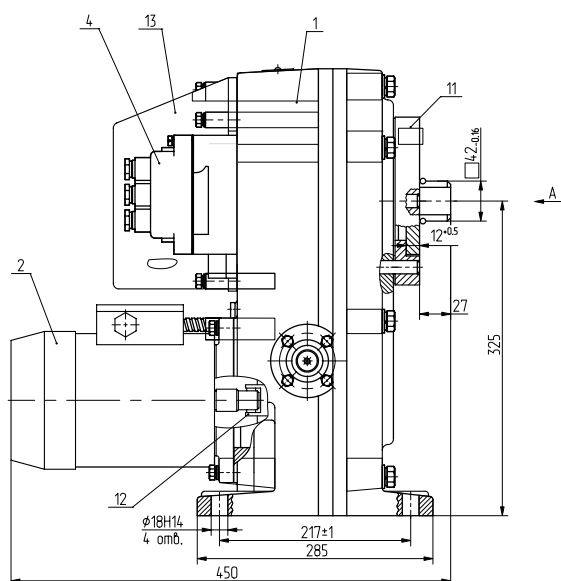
Габаритные и присоединительные размеры М30Ф-1000
